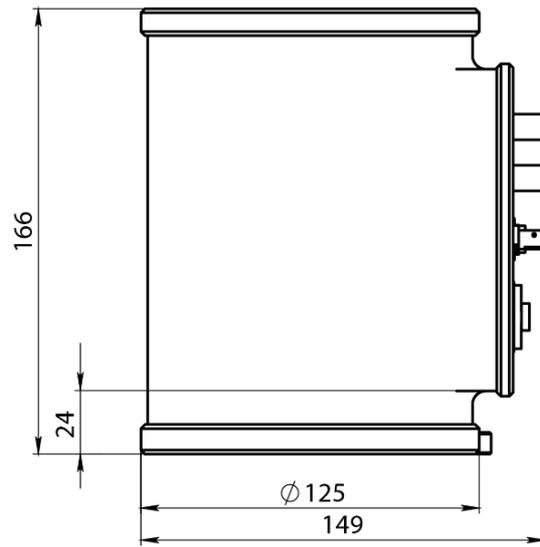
Robyhead D1 габаритные размеры нижней части.
